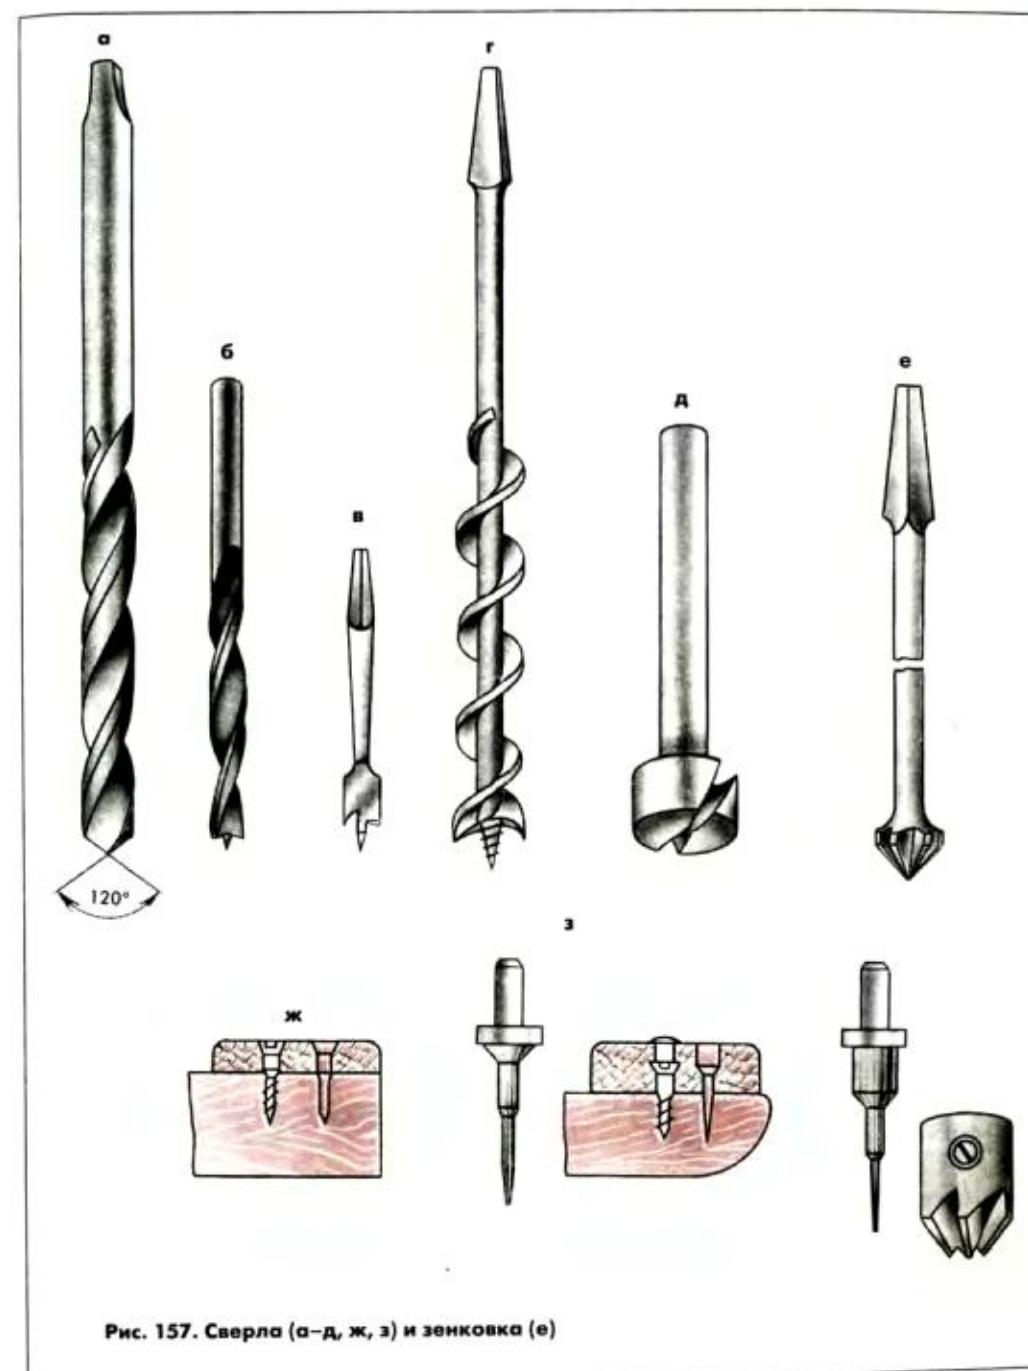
Сверла (а–д, ж, з) и зенковка (е)
